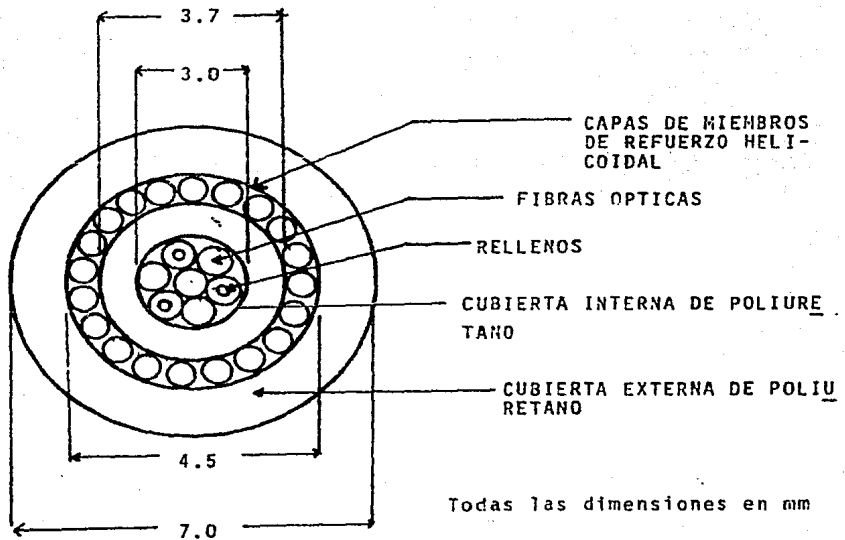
DISEÑO DEL CABLE DE FIBRA OPTICA
